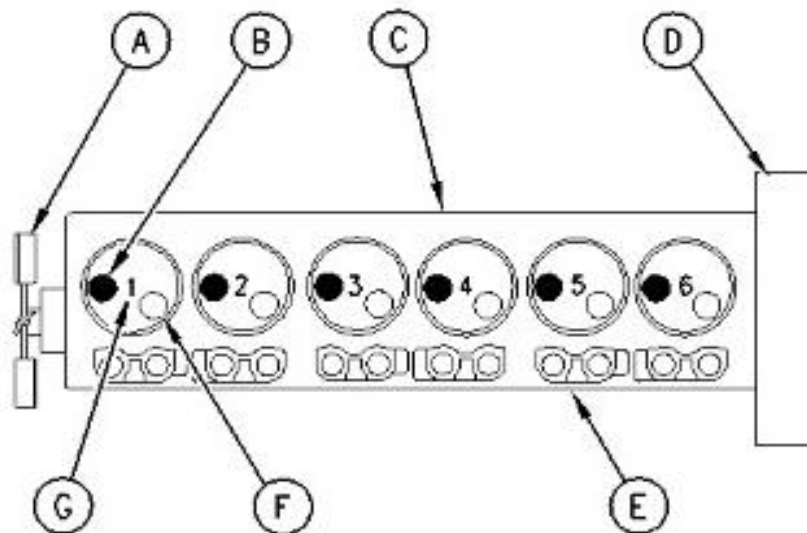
Vista superior del bloque de motor. Fuente: Manual de Operación Cat 3306.
